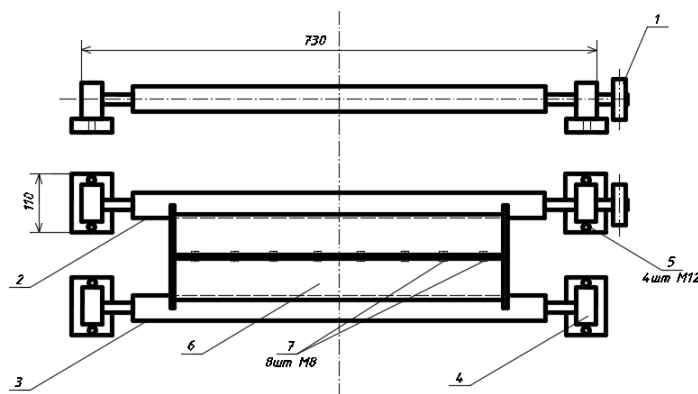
Принципиальная схема экспериментально-лабораторной центрифуги «ЦСРЛ-1», с формой: 1 – шкив привода центрифуги; 2 – ведущий опорный каток; 3 – ведомый опорный каток; 4 – упор вала опорной муфты с шарикоподшипником; 5 – крепеж упора к станине (с помощью болта M12); 6 – форма; 7 – соединение половинок формы (с помощью болта M12) (составлено авторами)
